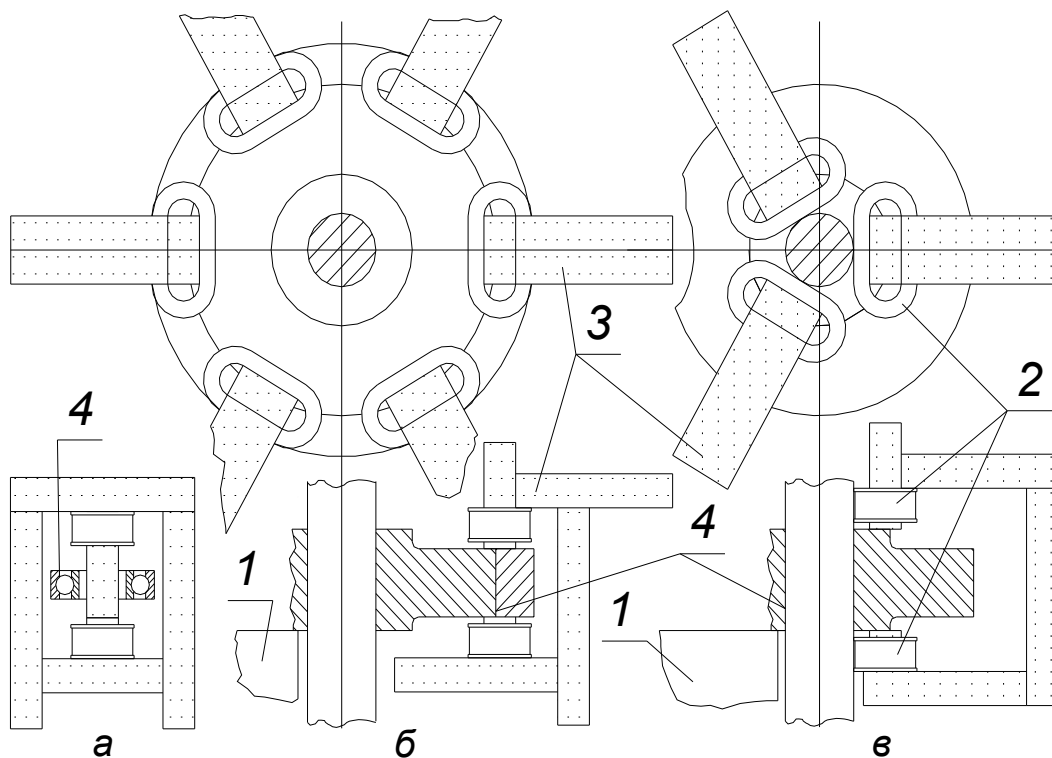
Универсальная индукционная установка для нагрева деталей под сборку и разборку
